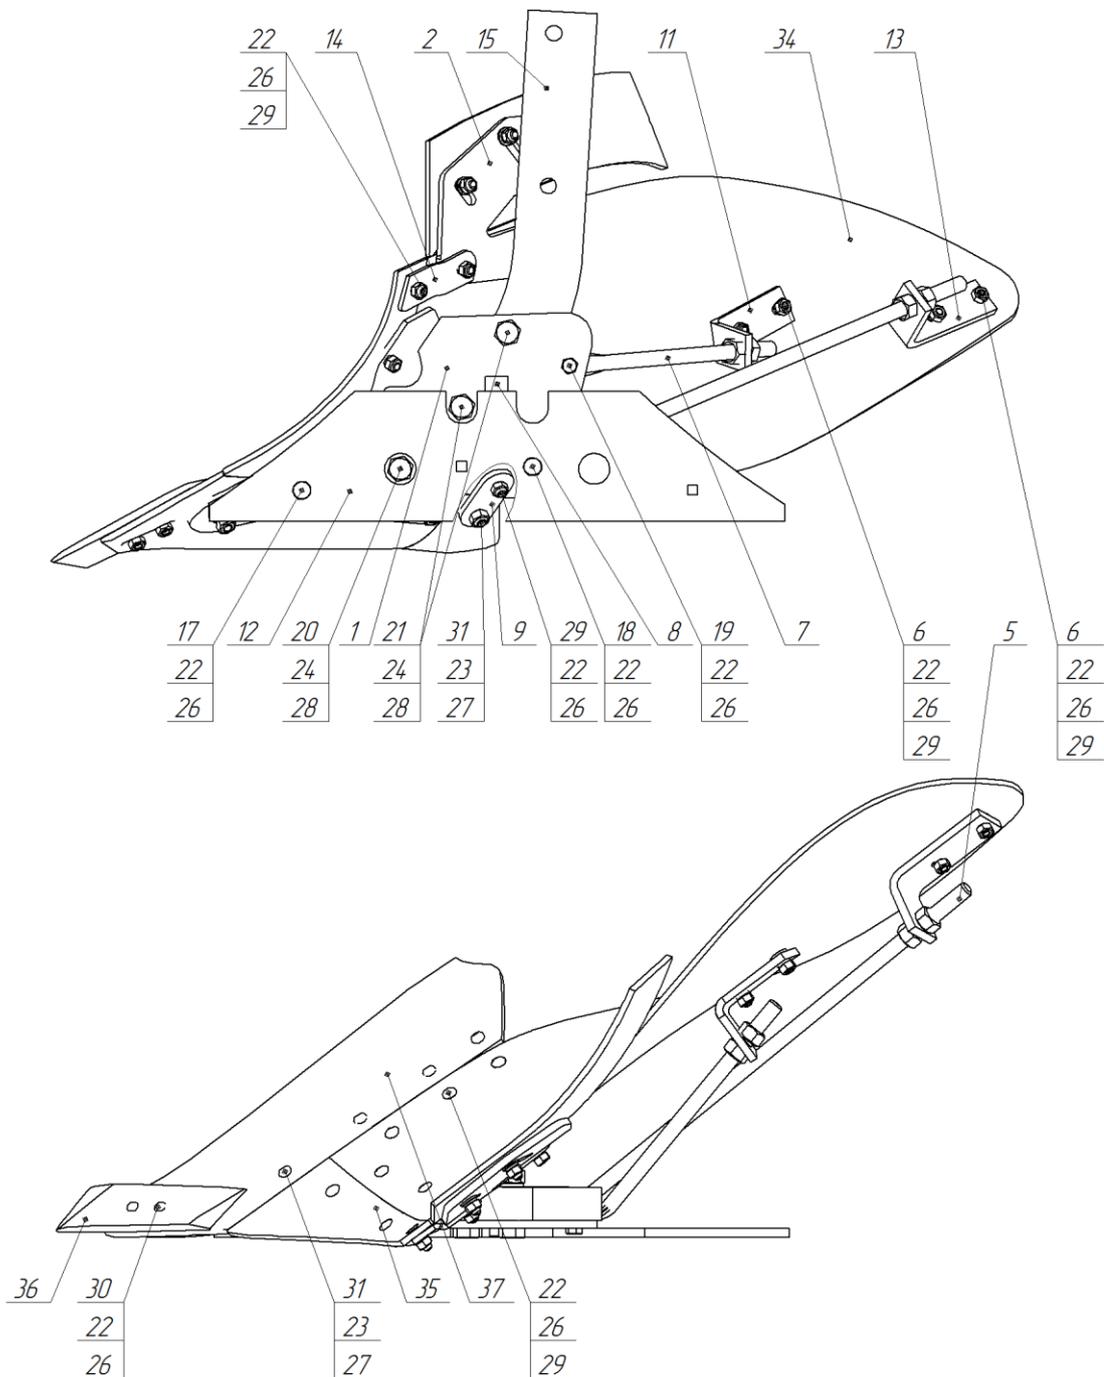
КСО-45 00.00.000 Корпус в сборе правый
